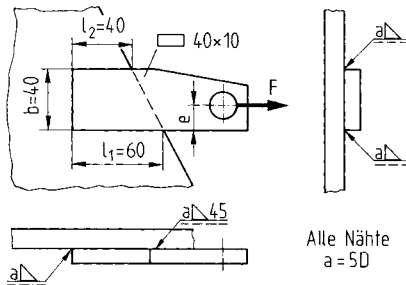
Schweißverbindung eines Flachstahls
